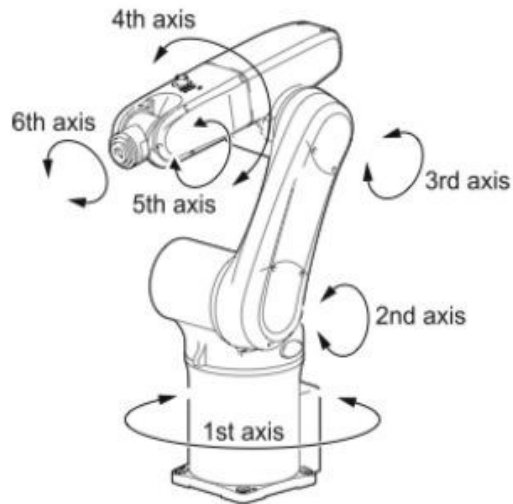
Příklad robota s otevřeným kinematickým řetězcem (How Are Industrial Robots Built? A Guide on the Components and the Movement of Robot Arms, 2018)
